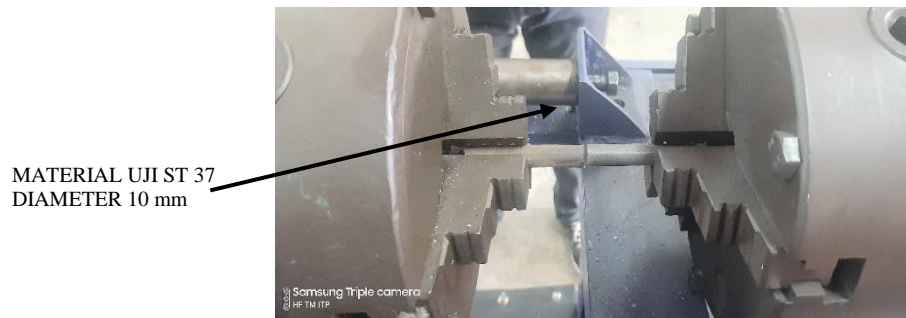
Konfigurasi Sambungan *Friction Rotary Welding
